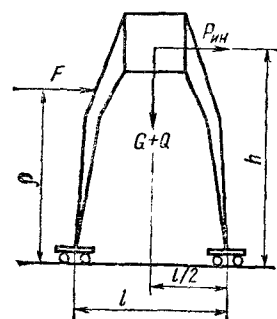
Схема к расчету устойчивости козлового крана в продольном направлении относительно кранового пути
